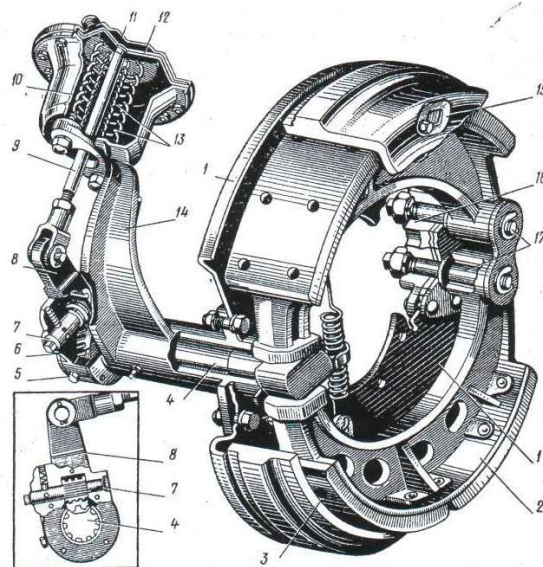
Колісний барабанний гальмовий механізм 1 – опорний диск; 2 – колодка гальма; 3 – гальмовий барабан; 4 – вал розтискного кулака; 5 – пробка отвору для мащення; 6 – черв'ячна шестерня; 7 – черв'як; 8 – важіль; 9 – шток гальмової камери; 10 – корпус гальмової камери; 11 – кришка гальмової камери; 12 – діафрагма; 13 – пружина; 14 – кронштейн гальмової камери; 15 – кришка люка; 16 – кронштейн вісі колодок; 17 – ексцентрикові вісі колодок.
